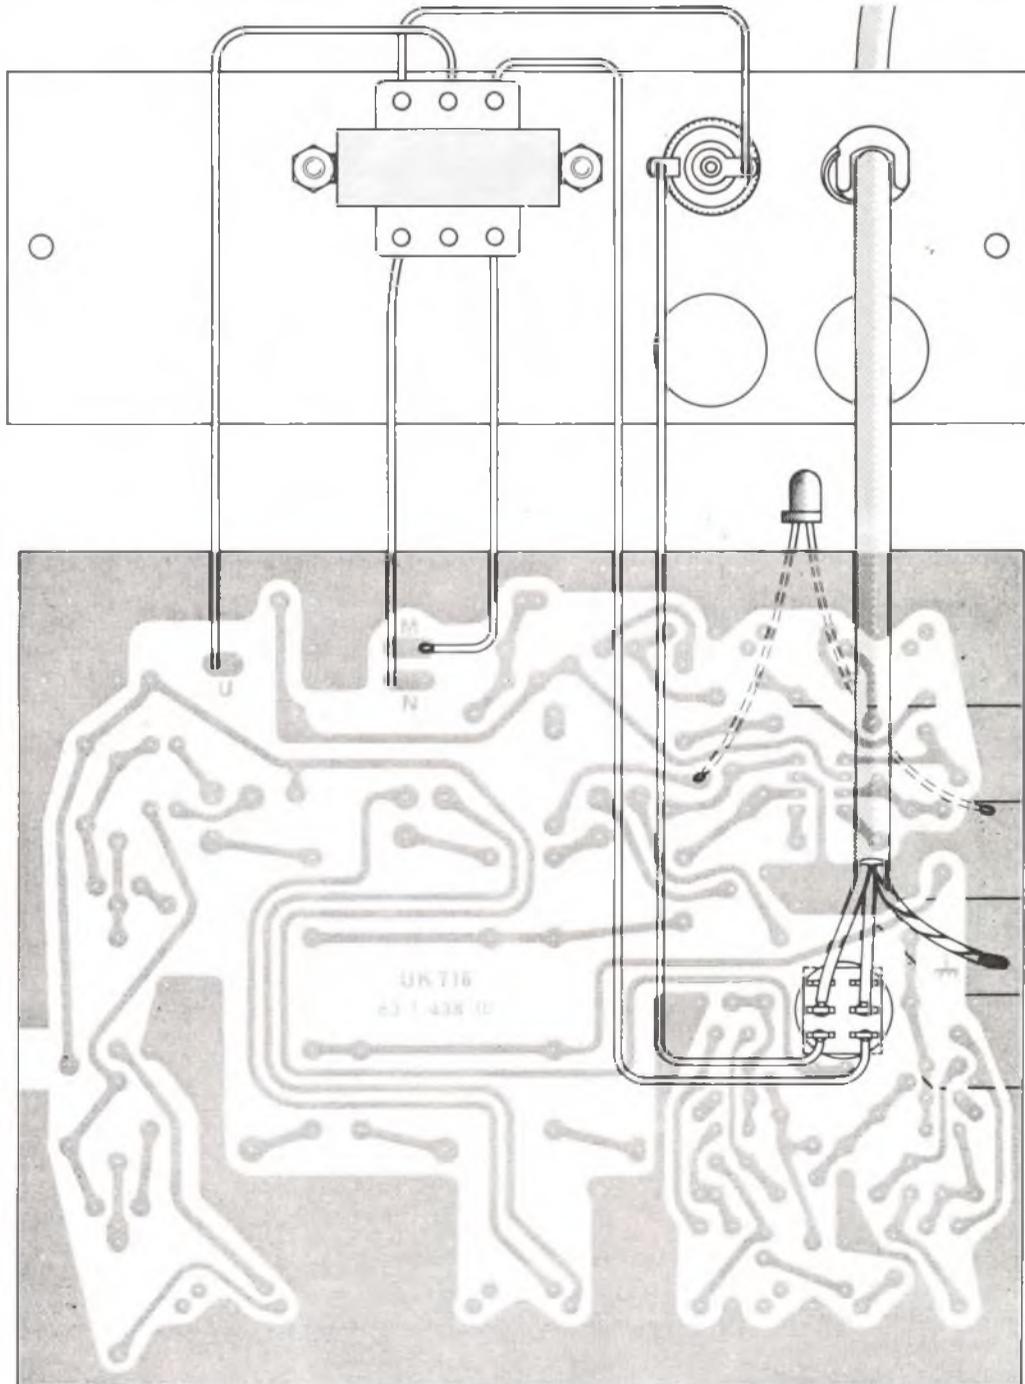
Cablaggio generale con le connessioni dettagliate impianto.
